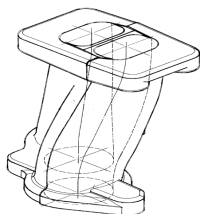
Заготовка детали 7406.1008 035 «патрубок левый автомобиля КАМАЗ»
